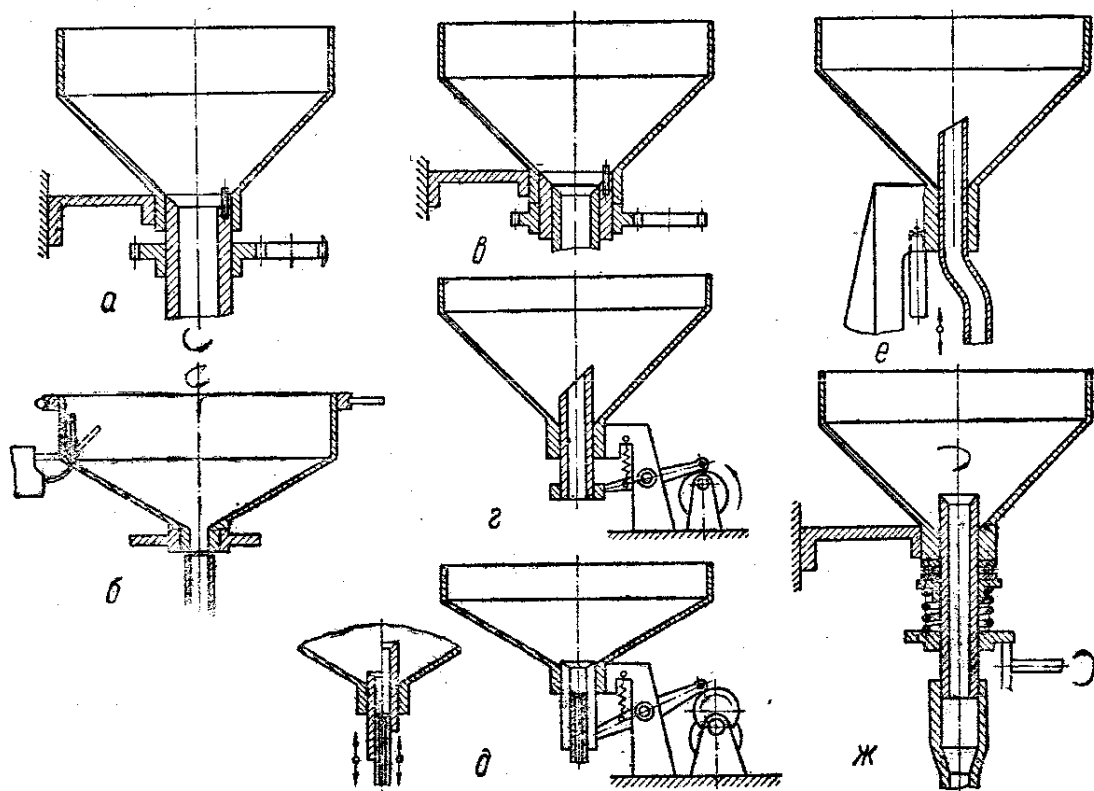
Типы трубчатых загрузочных устройств
